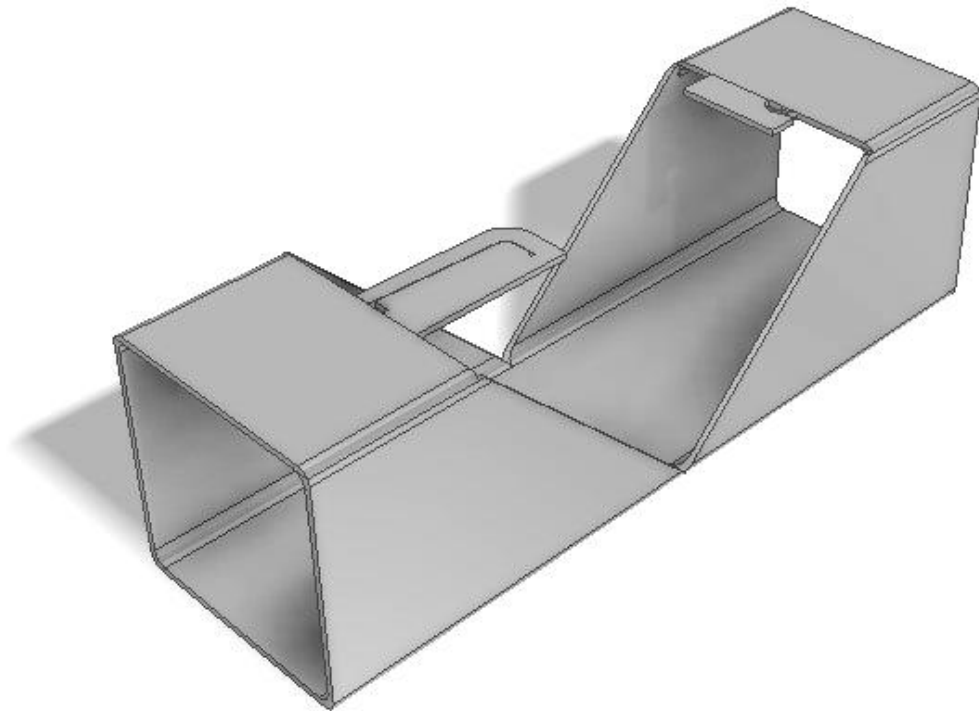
Dispositivo di bloccaggio snap-fit per il "Taglio-piega": incastro e Cantilever Beam.
